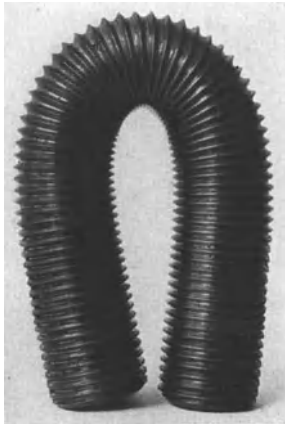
Gewindebiegeprobe aus Rotkupfer.
